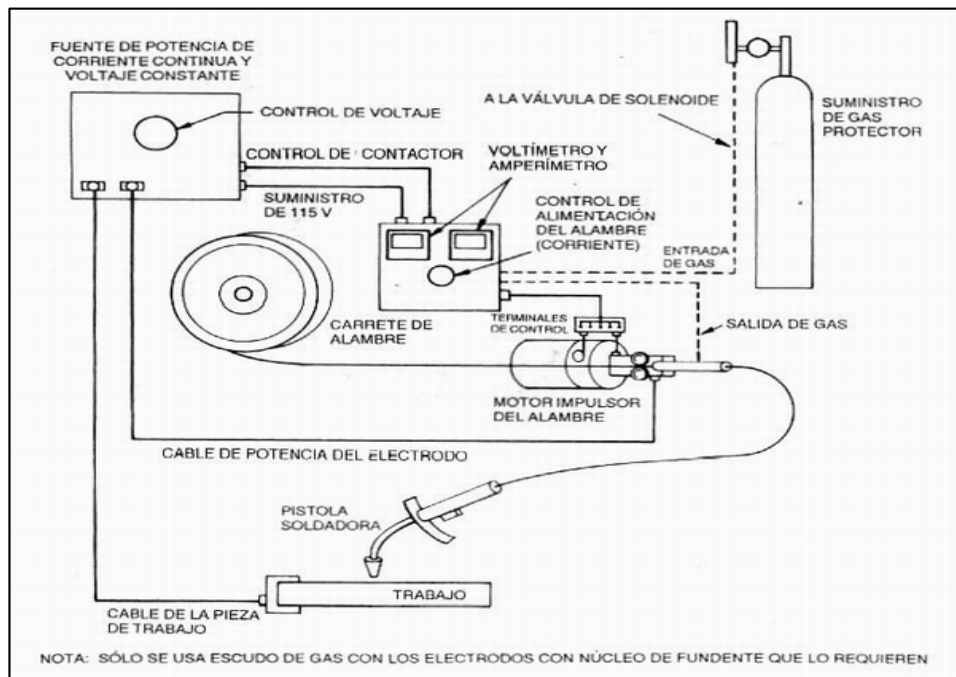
Procedimiento de soldadura FCAW.
